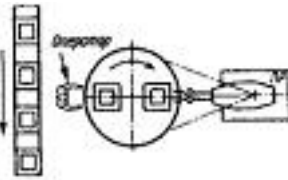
Схема сварочного комплекса с поворотным столом
